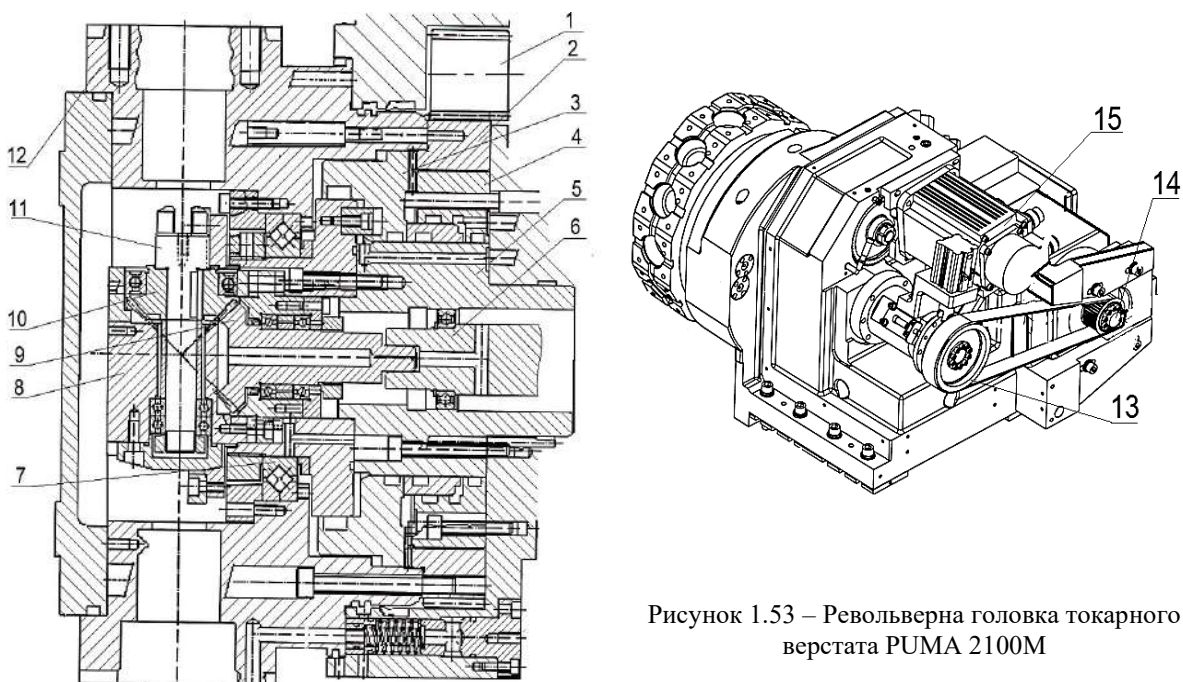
Револьверна головка токарного верстата PUMA 2100M
